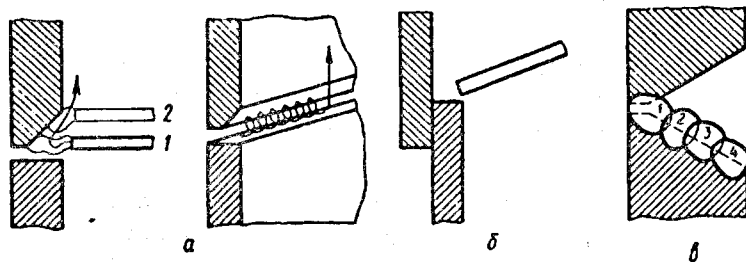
Сварка горизонтальных швов: а — стыкового соединения со скосом одной кромки; б — нахлесточного соединения; в — стыкового соединения со скосом двух кромок
